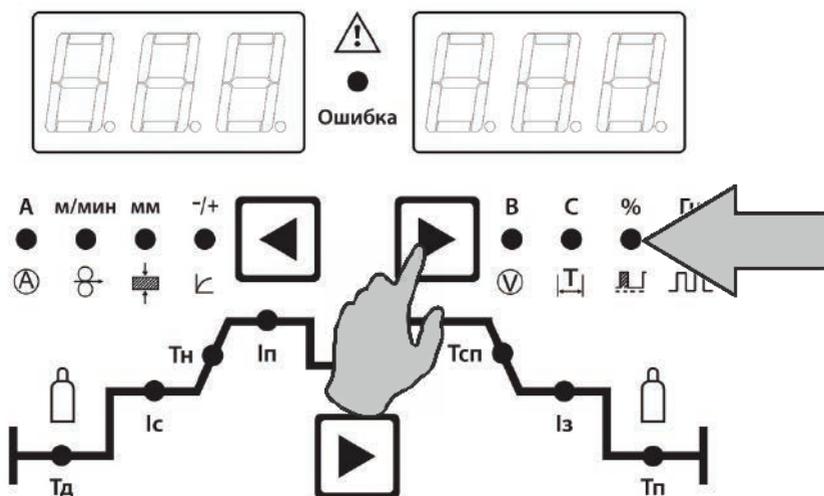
Установка времени продувки газом после сварки.
